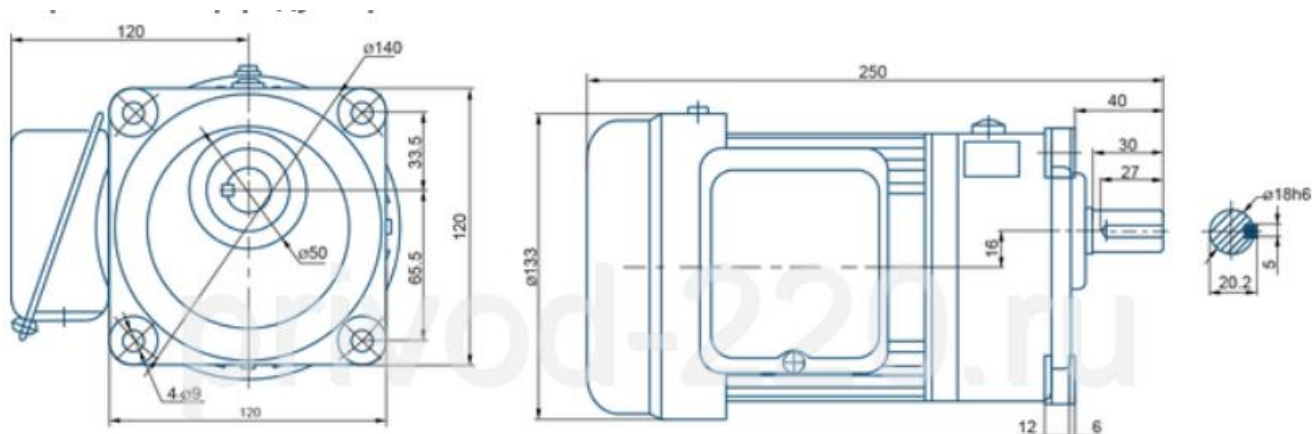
Чертеж мотор-редуктора 1# GV18-200W-20SB
